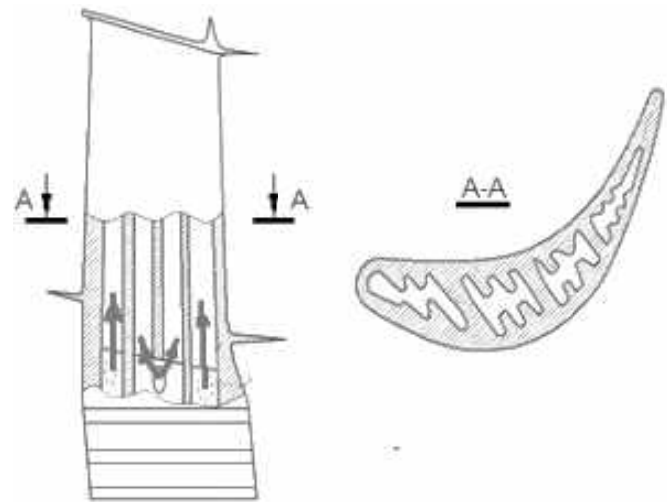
Поперечний переріз робочої лопатки двигуна Д-36
